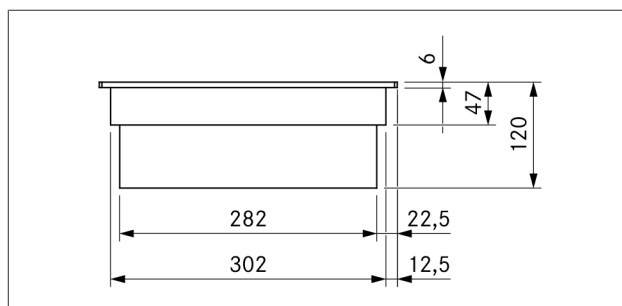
CKIW apparatets dimensjoner sett forfra
